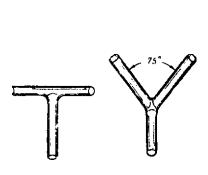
Изготовление соединительных трубок: а —опаивание двух заготовок перпендикулярно друг другу; б — сгибание заготовки под заданным углом и припаивание к ней отростка
